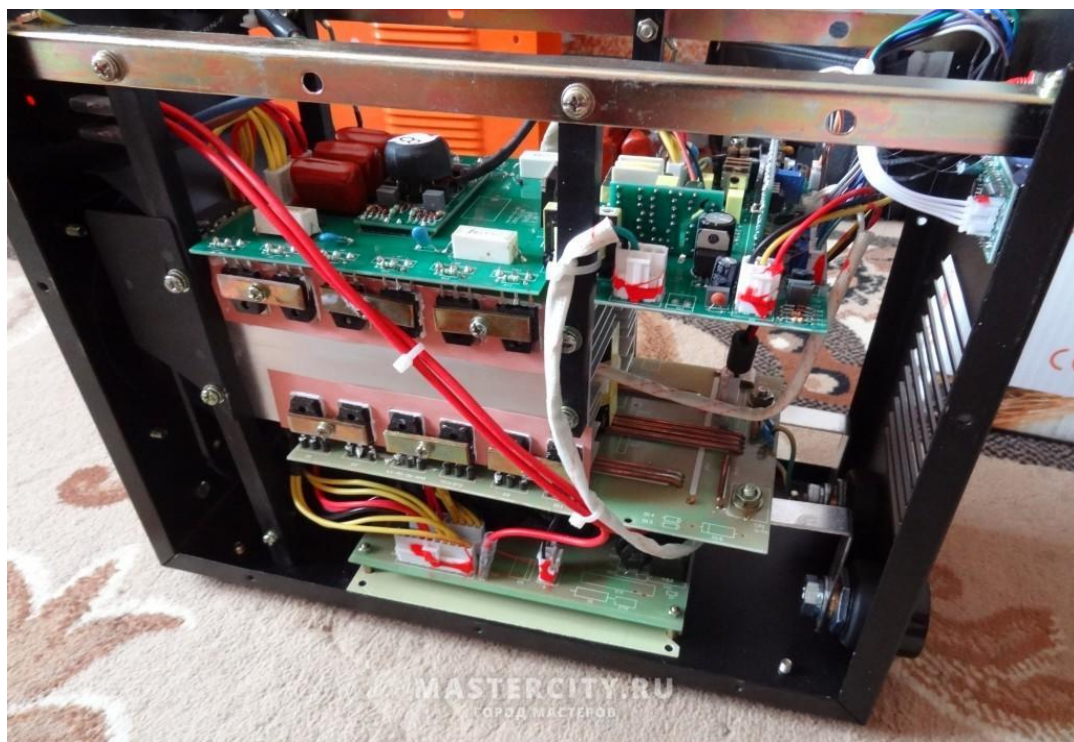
Внешний вид компоновки инвертора Ресанта.
